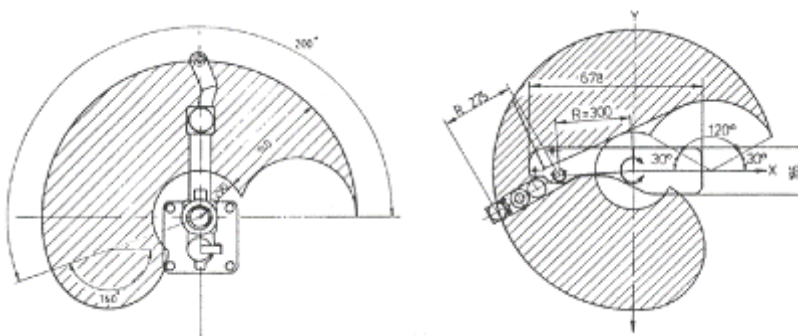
Robot seriale a geometria SCARA: vista in pianta e vista laterale
